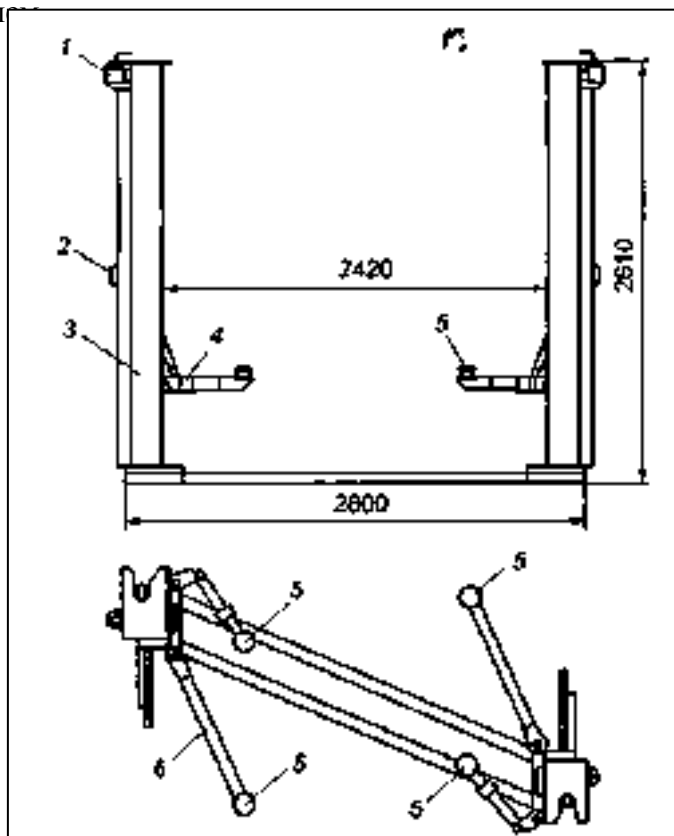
Напольный электромеханический двухстоечный подъемник П-133: 1 — электродвигатель; 2 — грузовая гайка; 3 — стойка; 4 — каретка; 5 — подхват; 6 — балка
